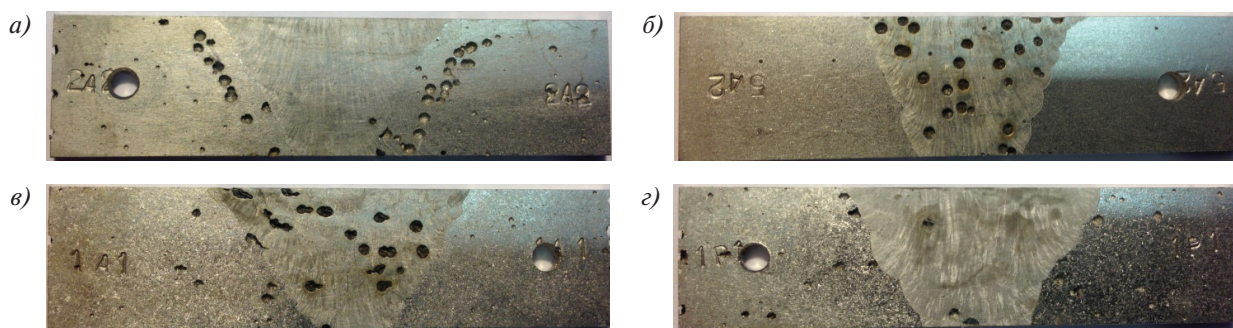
Распределение питтингов на поверхности образцов из сварных соединений стали X18H9, выполненных ручной аргонодуговой сваркой неплавящимся электродом с присадочной проволокой марки Св-04X17H10M2 (а-в) и ручной дуговой сваркой покрытыми электродами марки 48А-1 (г): а – плавка с 0,09С+0,02N; б – плавка с 0,06С+0,05N; в – плавка с 0,02С+0,09N; г – плавка с 0,02С+0,09N
